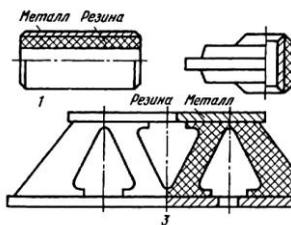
Резинометаллические детали: 1 – подшипник; 2 – пластинчатый амортизатор; 3 – амортизатор «ферма»
